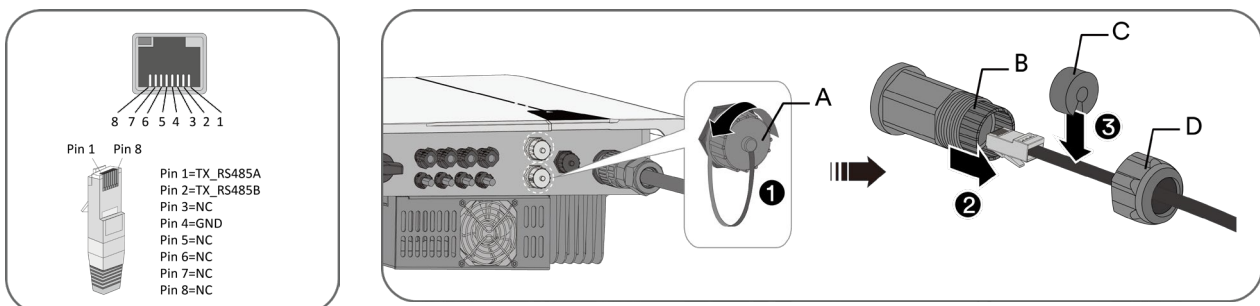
Kabelanschlussbelegung    Abb. 36. Netzwerkkabel einführen
